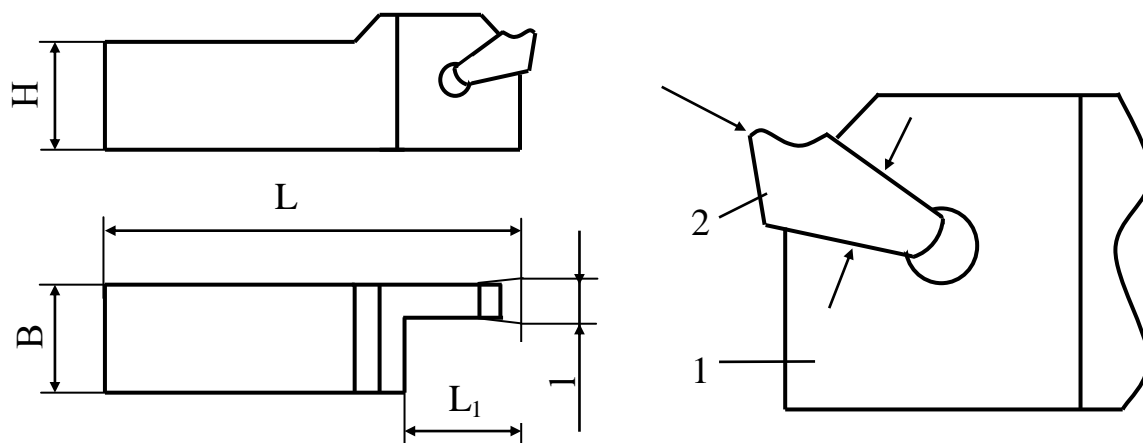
Сборный отрезной резец T-MAX Q-Cut
